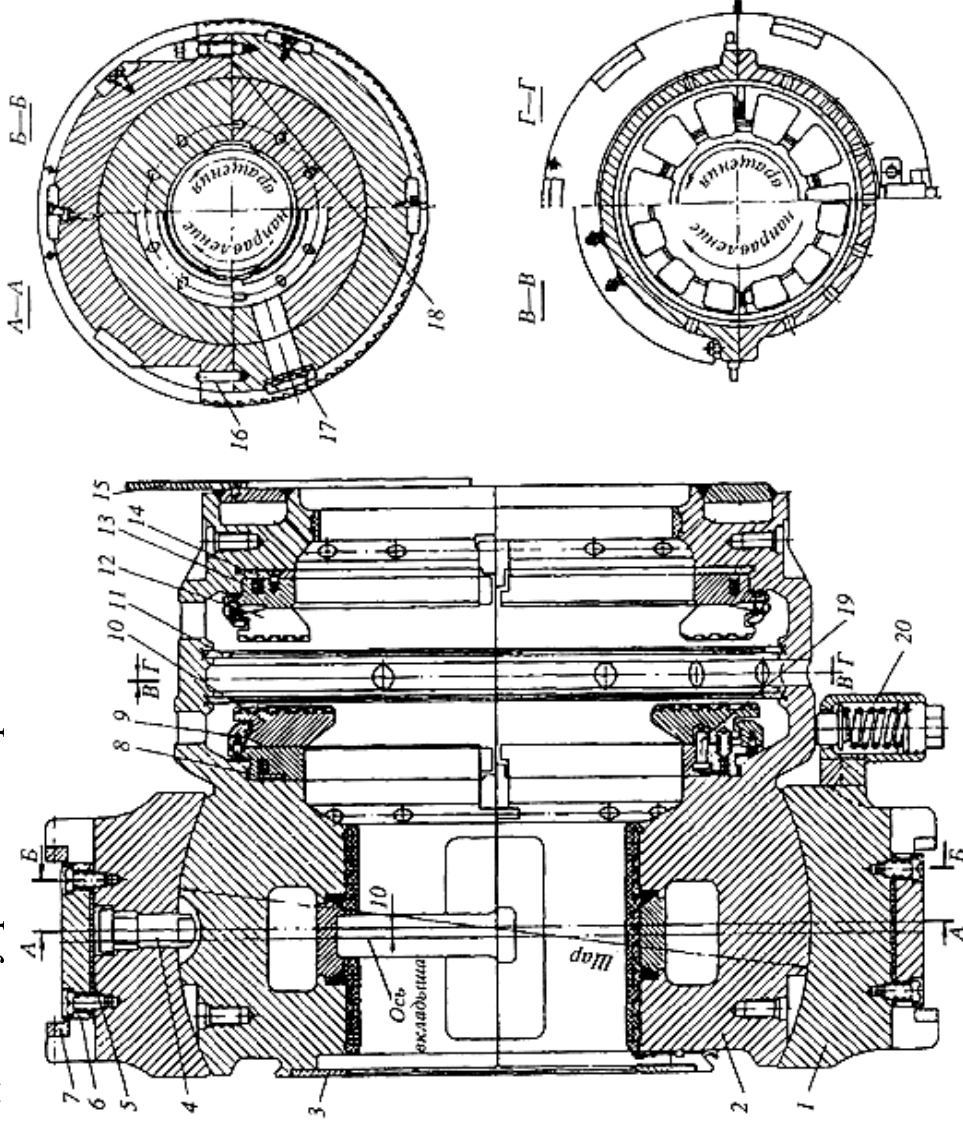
Опорно-упорный подшипник: 1 — сферический вкладыш; 2 — сферическая обойма вкладыша; 3 — маслоотбойное кольцо; 4 — стопор; 5 — винт; 6 — регулирующая колодка; 7 — установочное полукольцо; 9 — рабочее упорное полукольцо с защитным щитком; 8, 10 — рабочая колодка; 11 — гребешок уплотнения; 12 — установочная колодка; 13 — установочное упорное полукольцо с регулирующей прокладкой; 14, 15 — маслоотбойный щиток; 16, 19 — штифты; 17 — регулирующая колодка с дроссельной шайбой; 18 — крепежный болт; 20 — амортизатор
